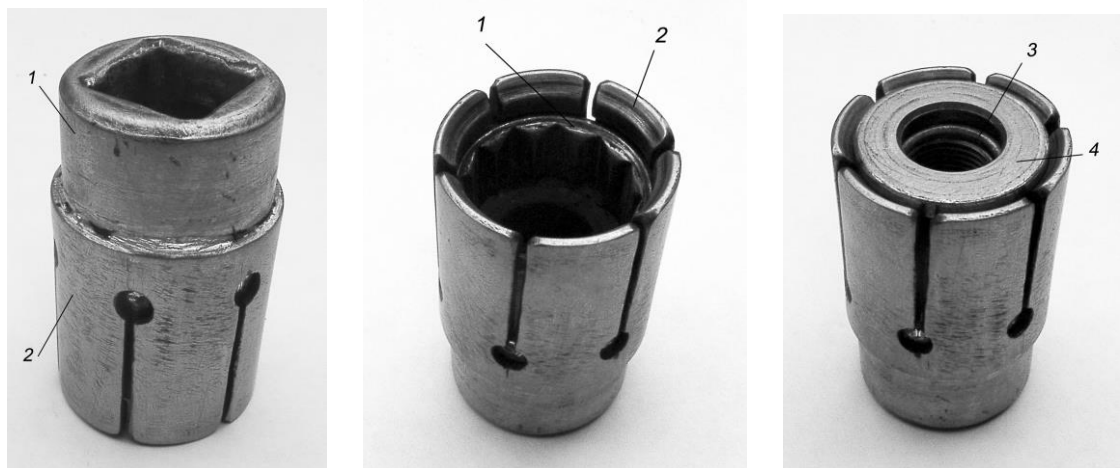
Головка для захоплення гайки з шайбою із касети: 1 – стандартна головка; 2 – цанговий тримач шайби; 3 – гайка М11×1; 4 – шайба 11.
